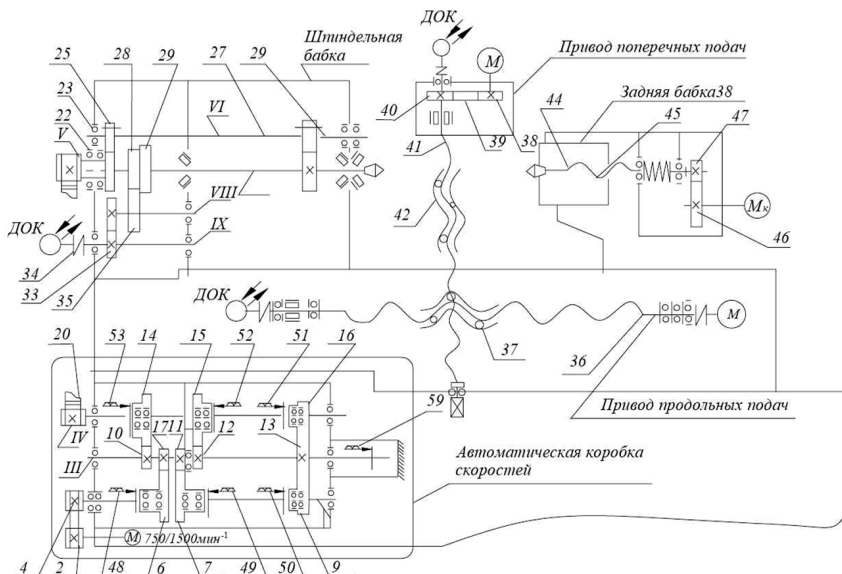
Кинематическая схема станка 16B16T1C1
